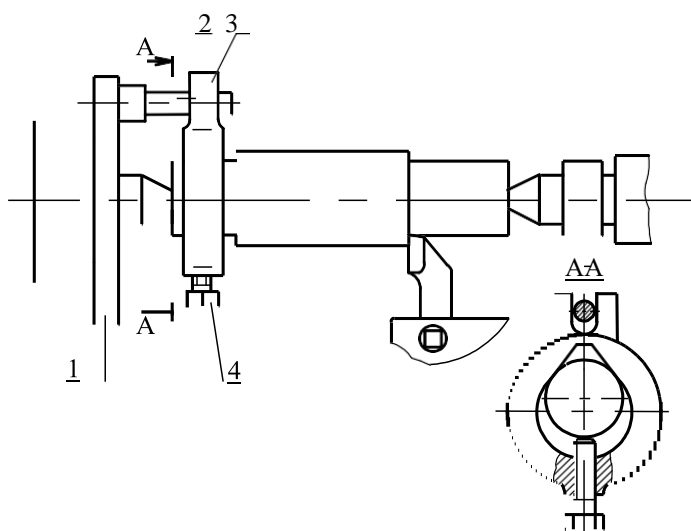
Обработка заготовки в центрах с приводом от поводкового патрона
